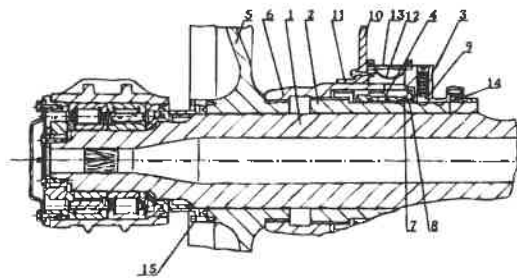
Схема конструкции РКП с жидкой смазкой
